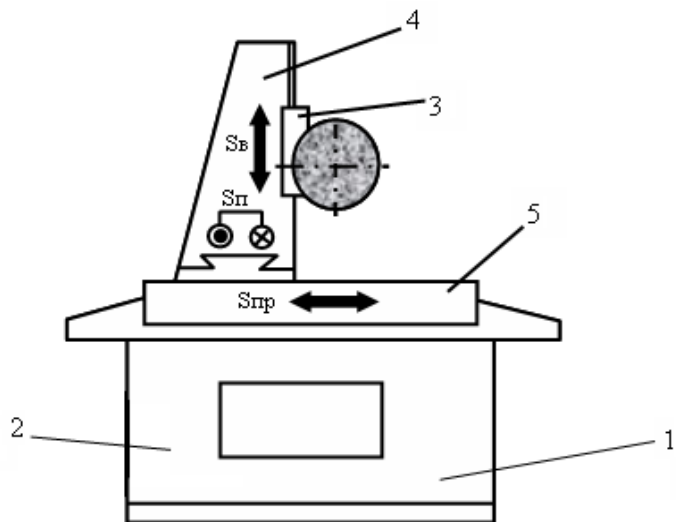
Общий вид плоскошлифовального станка с прямоугольным столом
